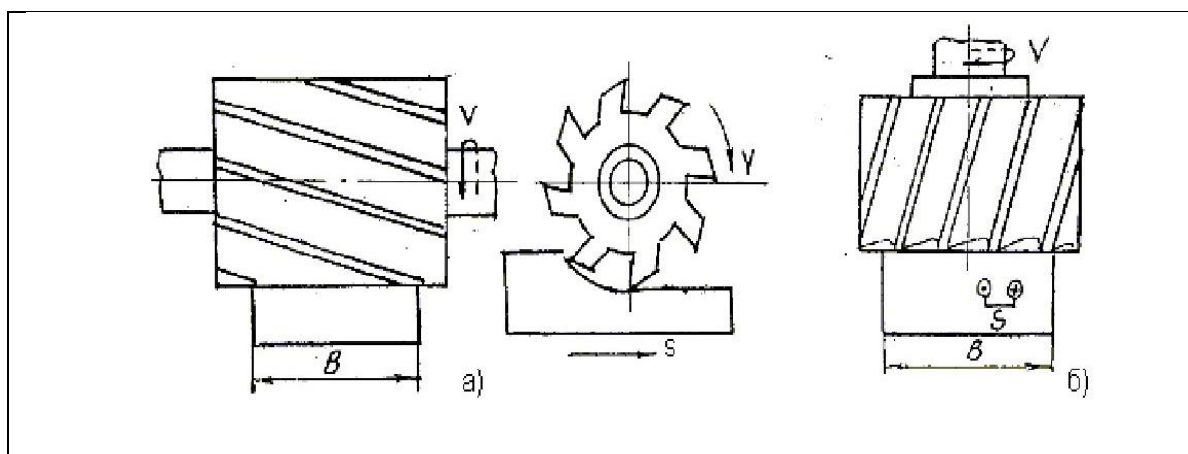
Схеми фрезерування площин фрезою (а-циліндрично, б-торцевою)
